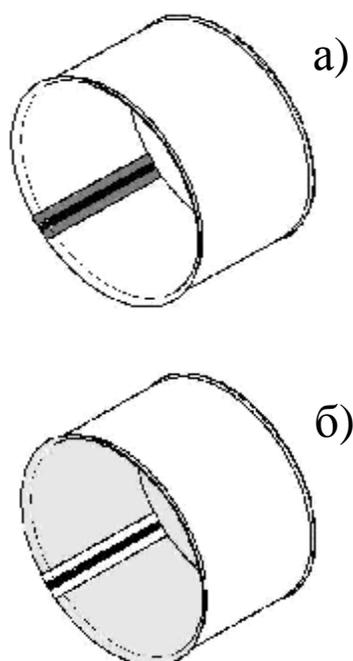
Образцы банок для оценки коррозионной стойкости: а) всей внутренней поверхности банки за исключением зоны сварного шва; б) участка сварного шва
